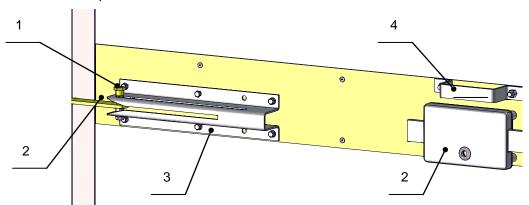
Внешний вид двери с внутренней стороны 1 -Фиксатор; 2 - Планка фиксатора; 3 - Направляющий профиль; 4 - Ручка двери; 5 - Запорный механизм
